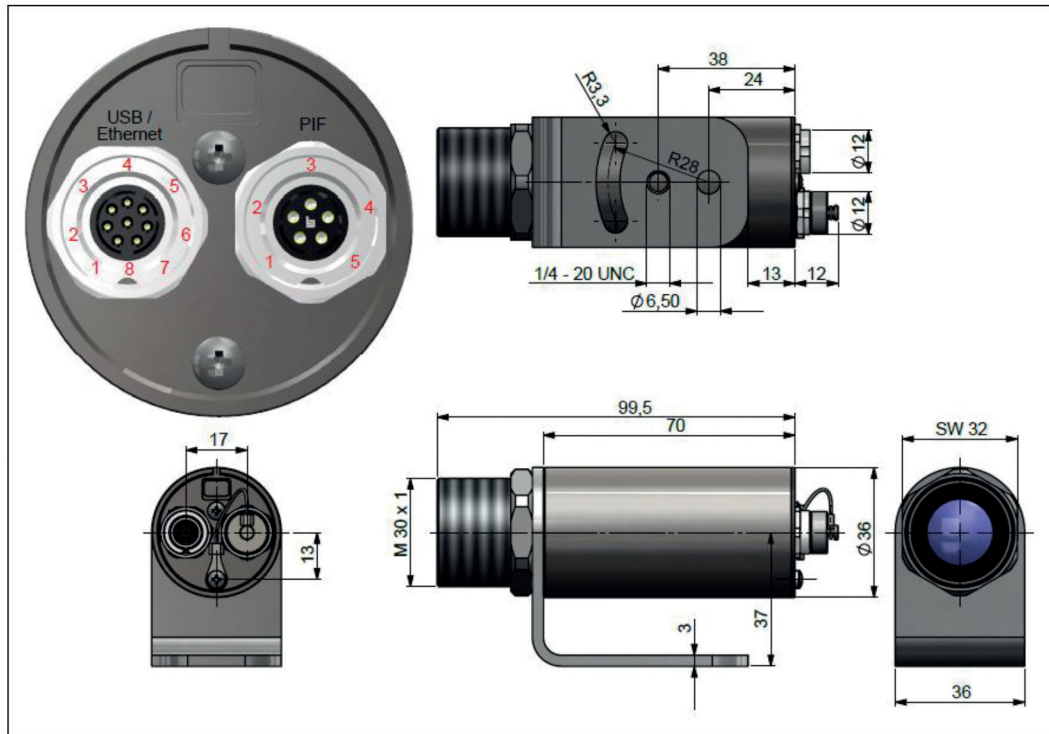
Maßzeichnung thermoIMAGER TIM 41, Abmessungen in mm
